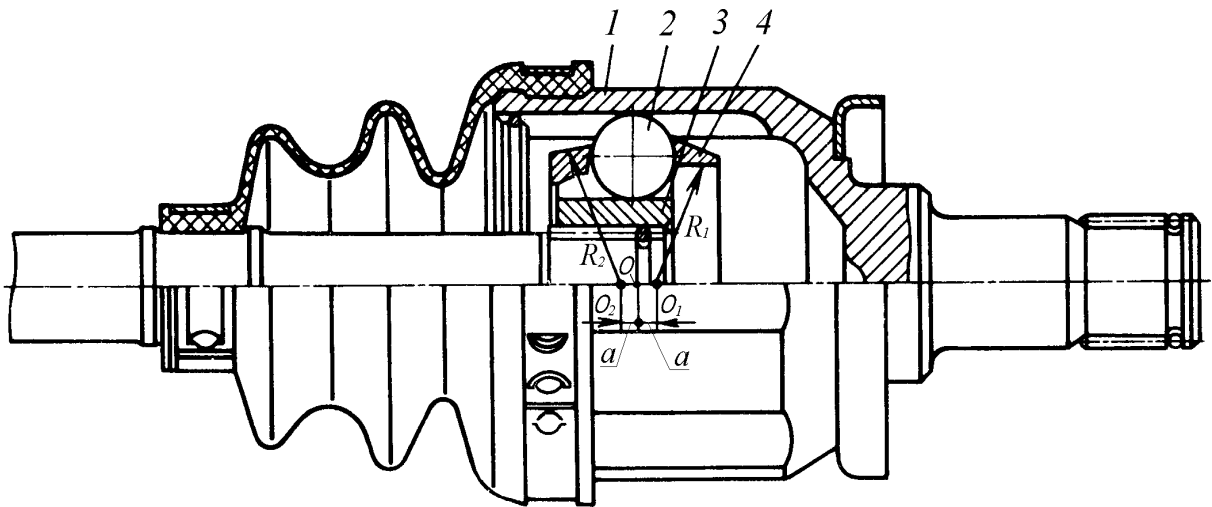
Шестишариковый универсальный карданный шарнир типа ГКН:
